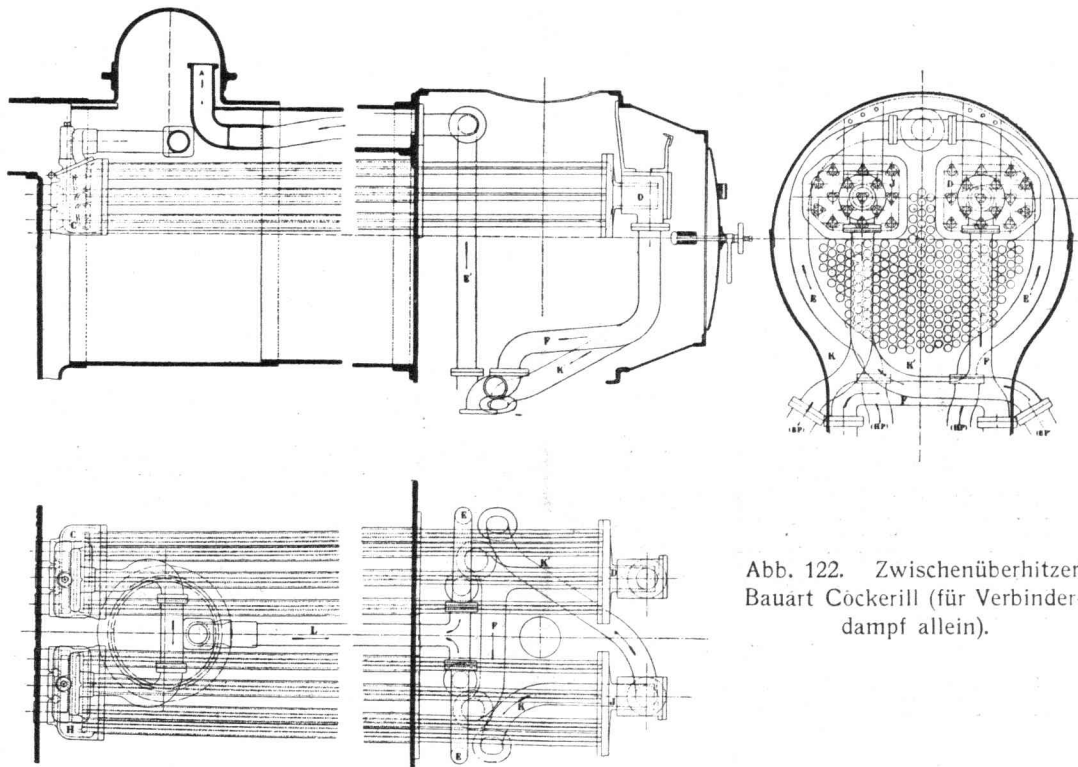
Zwischenüberhitzer, Bauart Cockerill (für Verbinderdampf allein).
